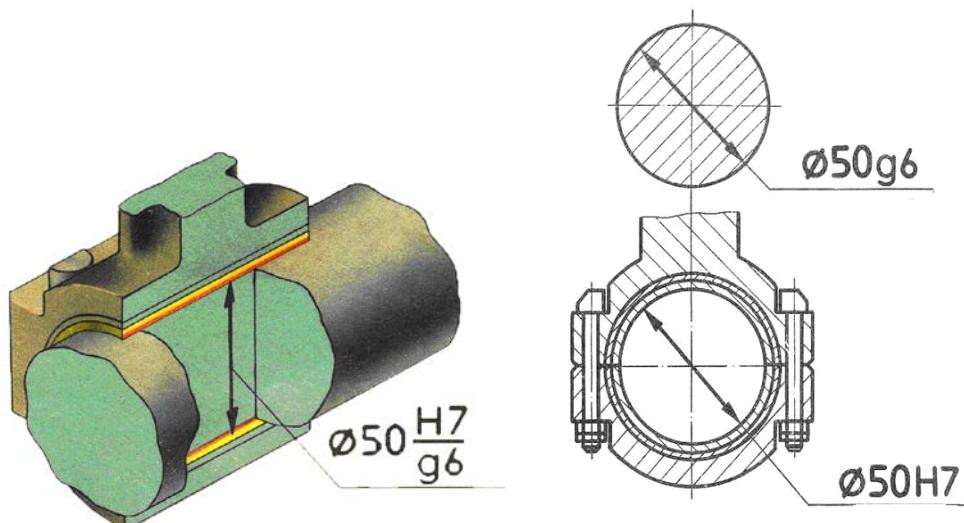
Шейка коленчатого вала со втулкой головки шатуна
